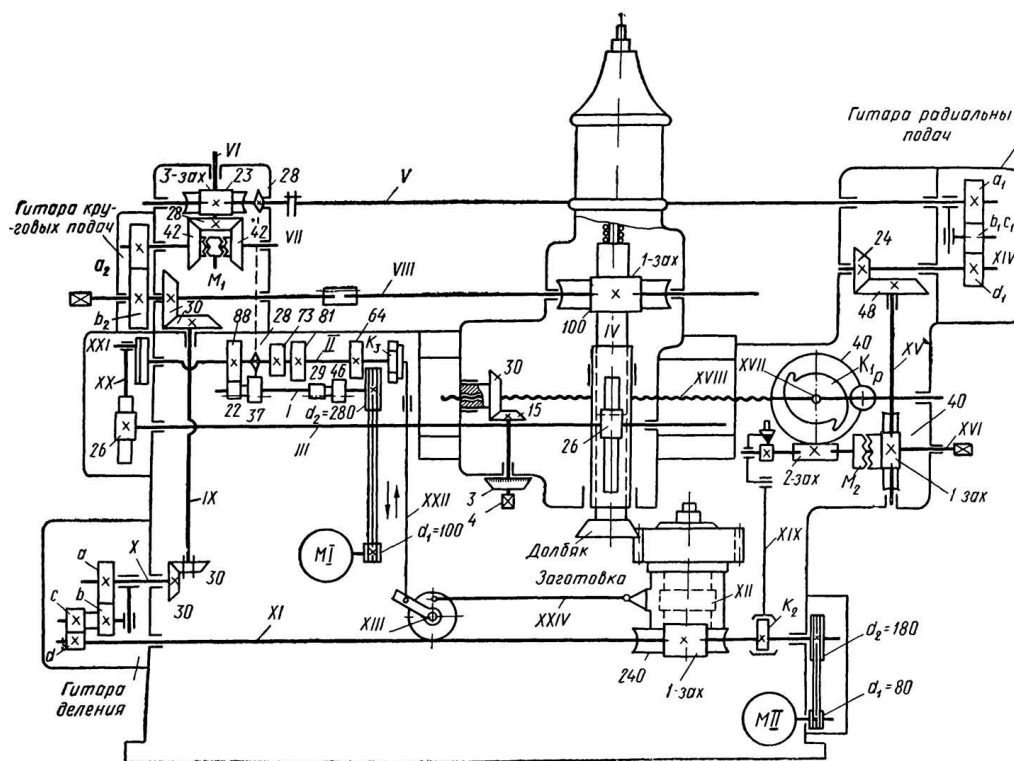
Кинематическая схема зубодолбежного станка 514
